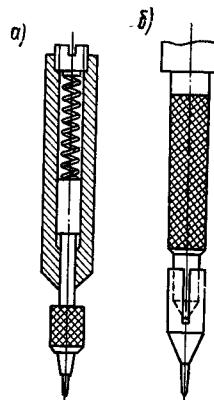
Плавающий карандаш (а) и чертилка (б) для копировального пальца
